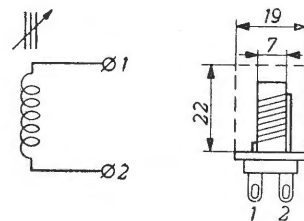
Dimensioni dell'induttanza  $L_5$  e del suo supporto con schermo.
